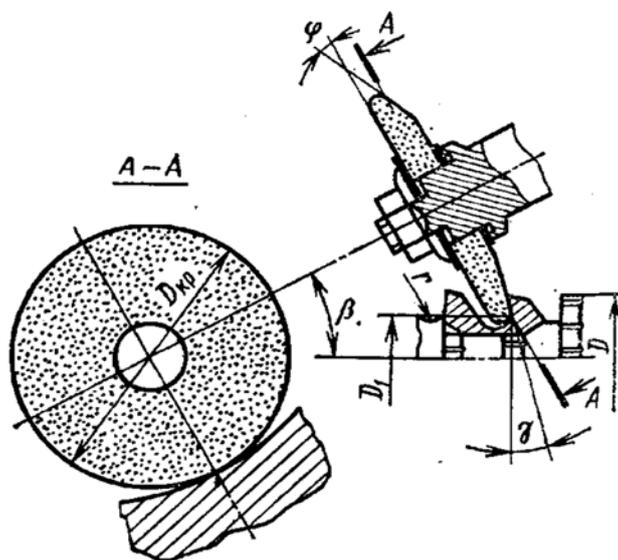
Схема заточки зуба круглой протяжки по передней поверхности
